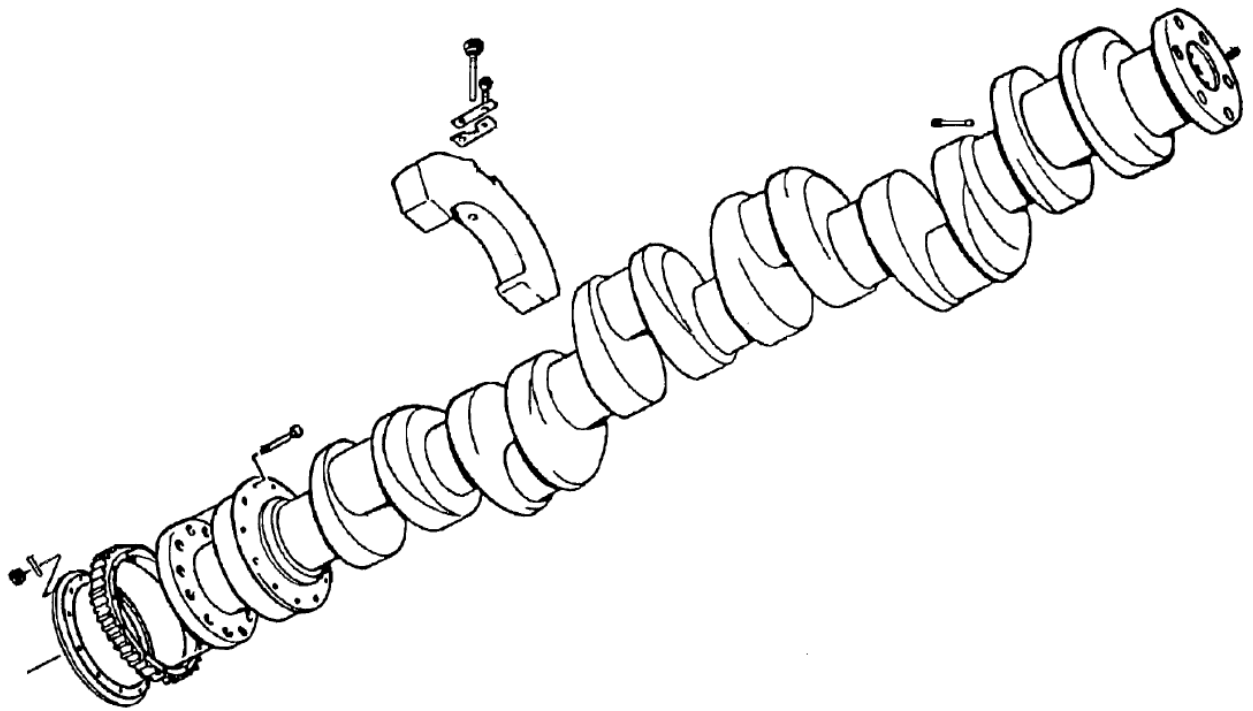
Колінчатий вал двигуна L28/32
